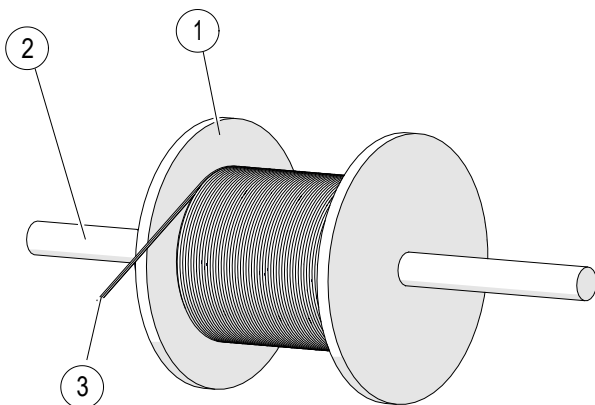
Aufgewickelter Heizleiter mit Aufhängung
